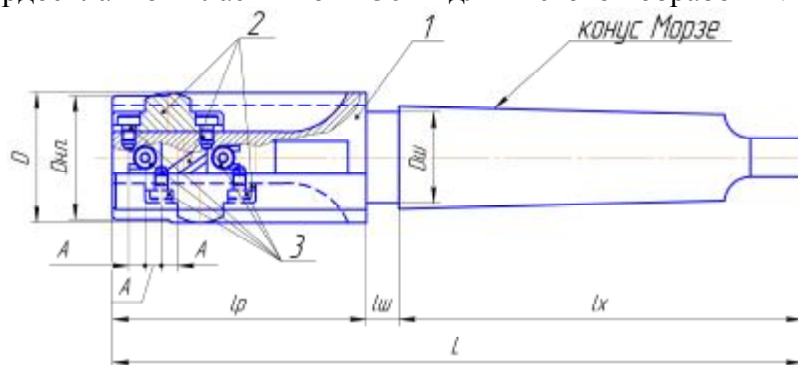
Конструкция усовершенствованной резцовой сборной развёртки с безвершинными зубьями, общий вид
